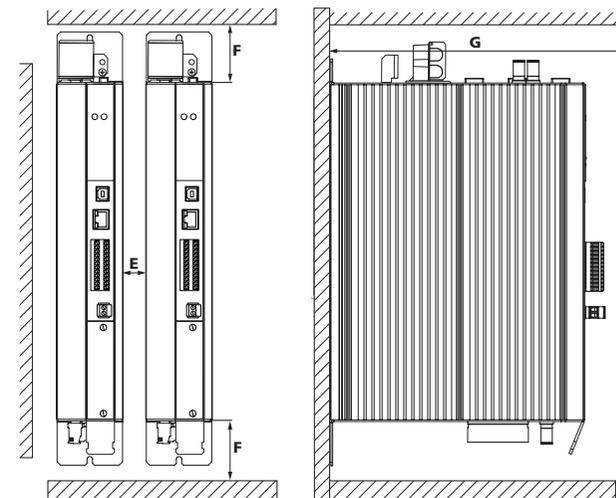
Montageabstände Gehäusevariante Luftkühlung
